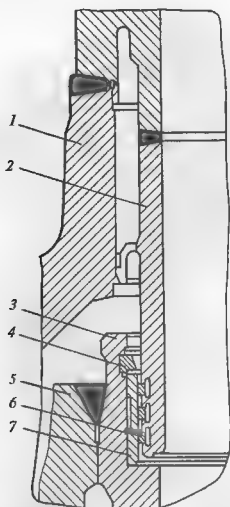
Конструкция паровпуска двухстенного ЦВД
